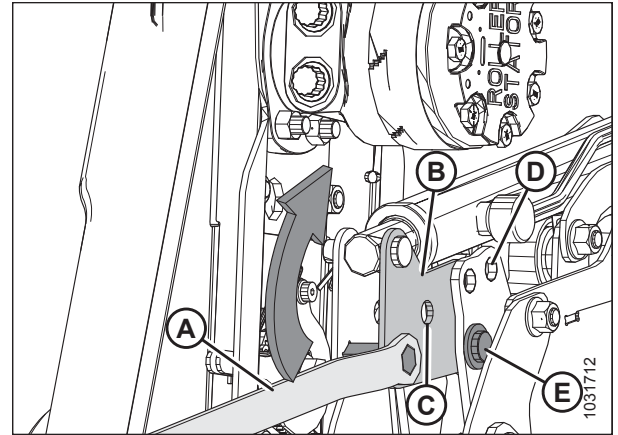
Cilindru brațului central stâng – poziția înainte
